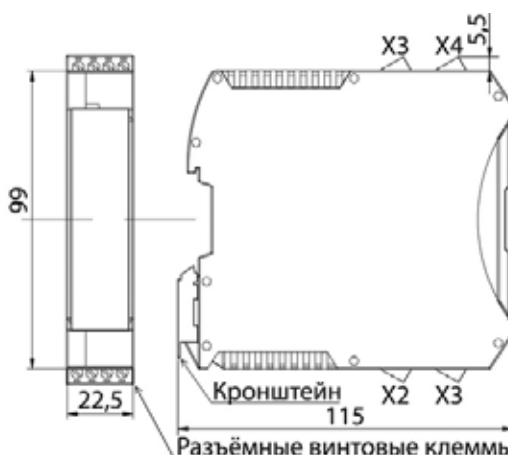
НПСИ-230-УНТ: габаритные размеры и крепление к DIN-рейке
